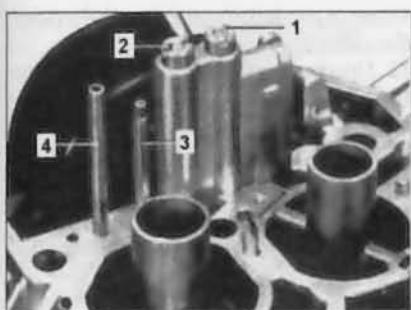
Верхний корпус карбюратора 2E2 (перевернутый), расположение жиклеров (Глава 10)
